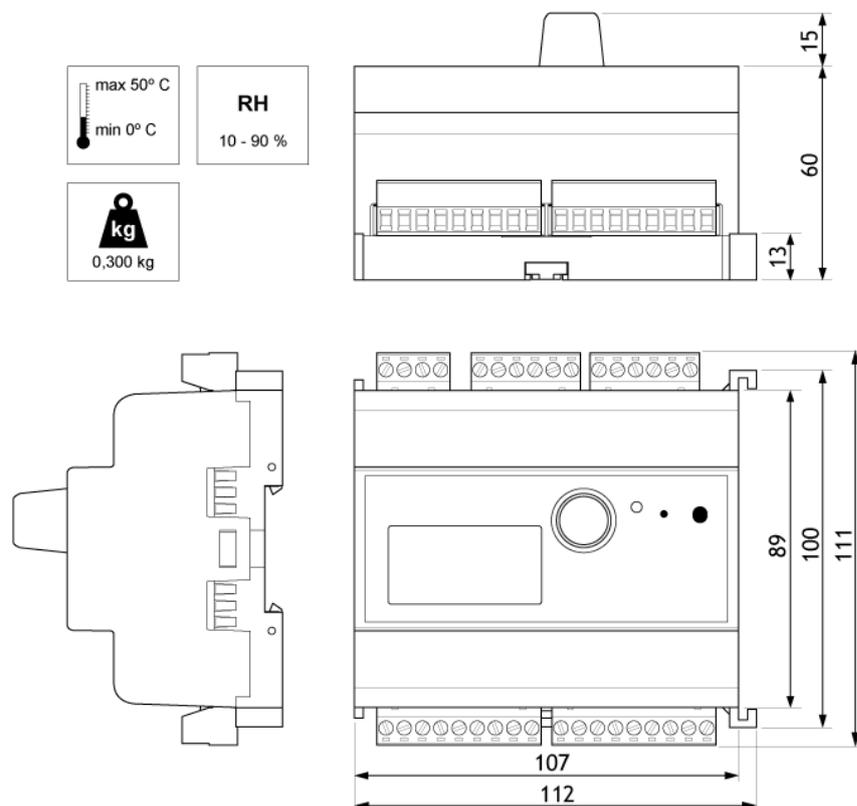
LIOB-180 Gehäuse (Abmessungen in mm)
